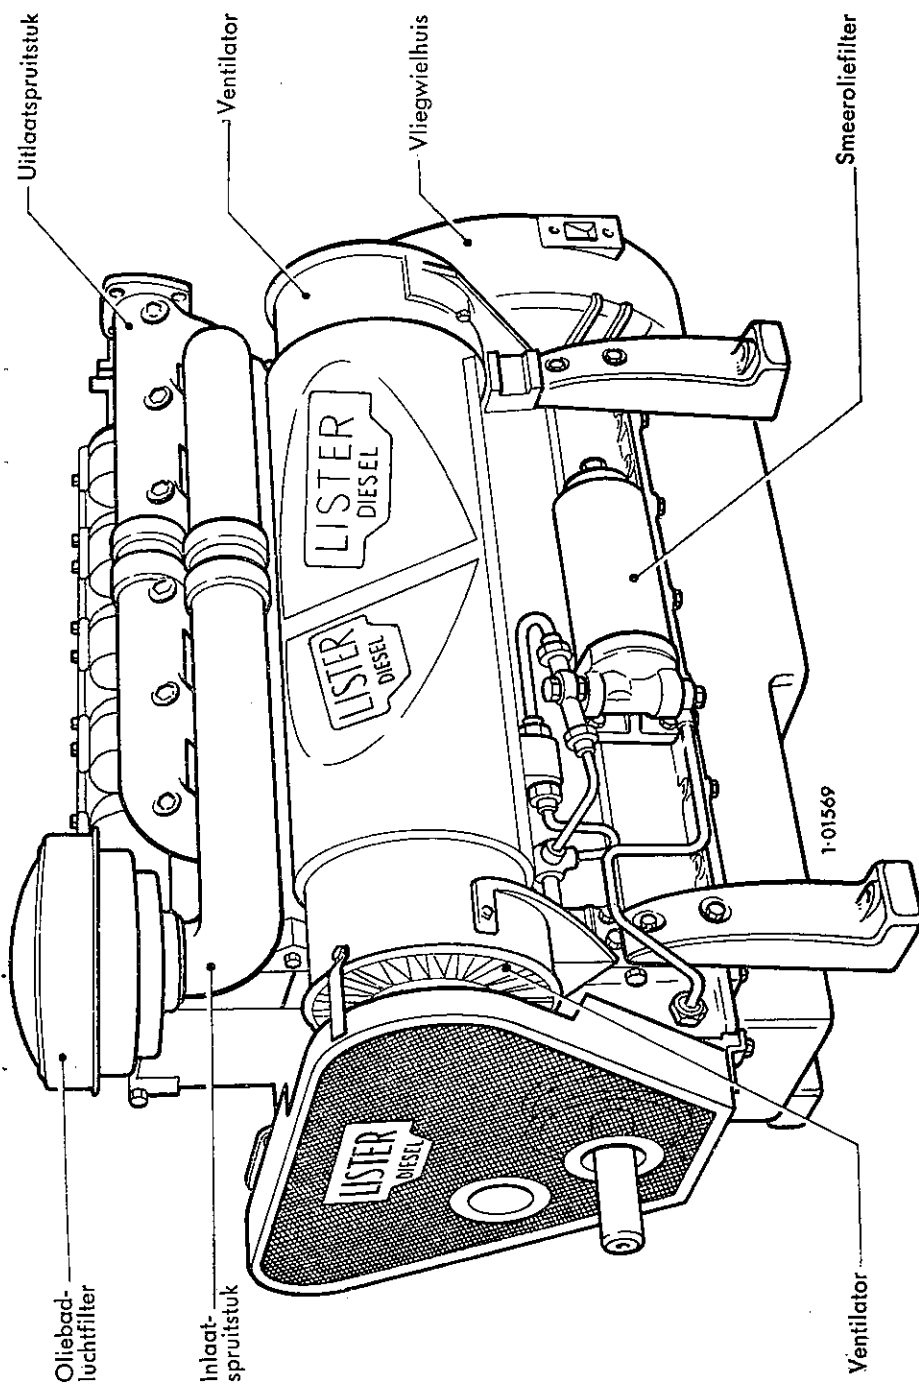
HA 6/HB 6 luchtgekoelde dieselmotor
